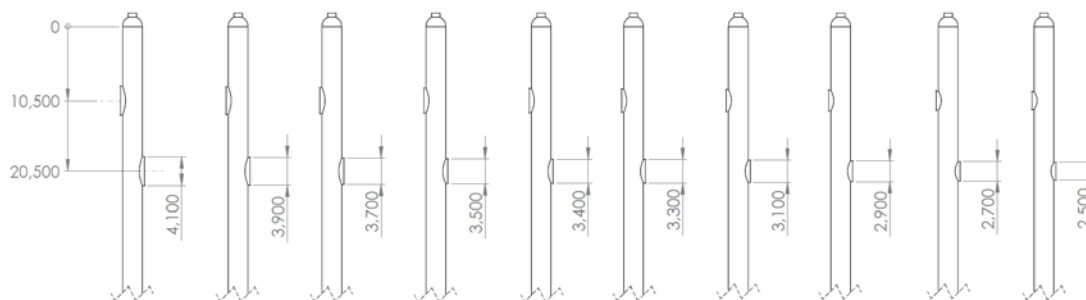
Sondas criadas para verificação do parâmetro 1 - Área de entrada. Dimensões em mm.
